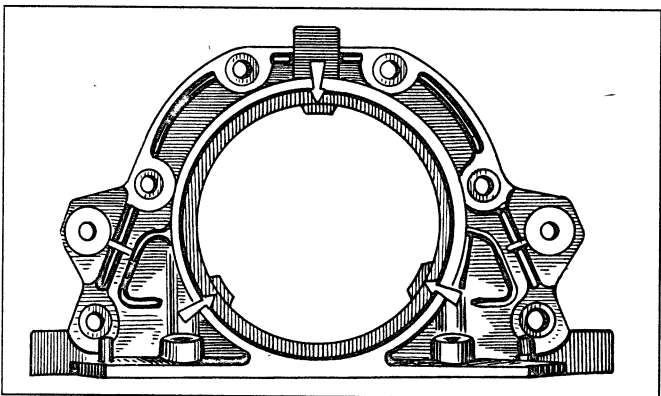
Держатель заднего сальника коленчатого вала. Стрелками показаны выступы для центрирования держателя относительно фланца коленчатого вала
